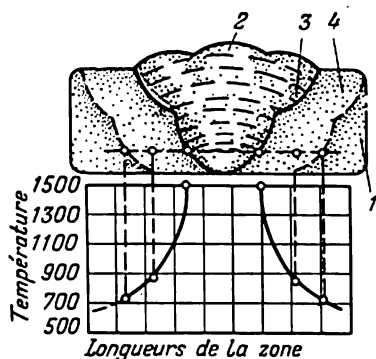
Structure d'une soudure et répartition de la chaleur lors du soudage de l'acier
